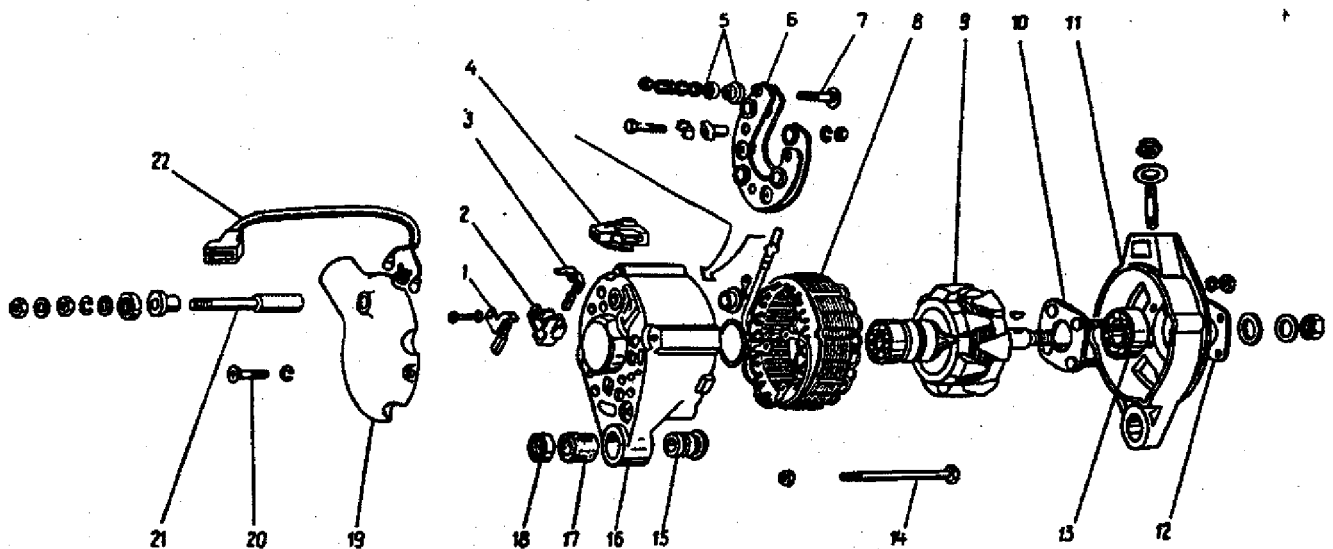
Componentes do alternador: 1 - escova negativa; 2 - porta-escovas; 3 - escova positiva; 4 - sapata do terminal do conector neutro; 5 - buchas; 6 - bloco retificador; 7 - parafuso de contato; 8 - estator; 9 - rotor; 10 - flange de retenção do rolamento dianteiro; 11 - tampa dianteira; 12 - flange externo de retenção do rolamento; 13 - rolamento dianteiro; 14 - parafuso de união; 15 - casquilho de aperto; 16 - tampa traseira; 17 - bucha interna; 18 - bucha externa; 19 - tampa protetora; 20 - parafuso de fixação da tampa; 21 - prisioneiro das conexões; 22 - chicote com conectores.
